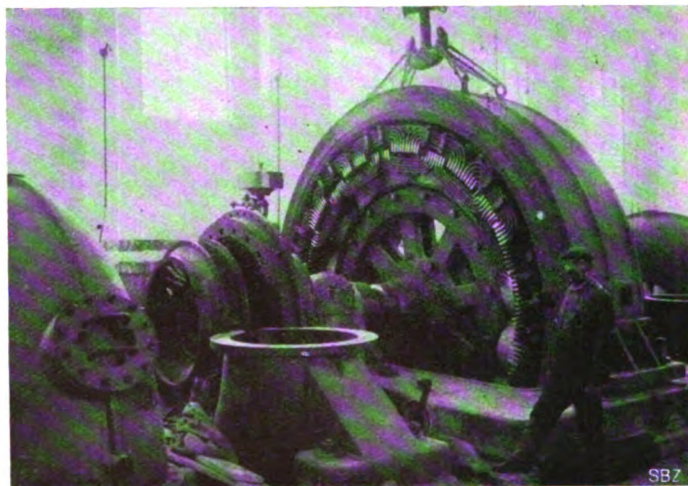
Maschinengruppe im Bau (5000 PS-Turbinen-Laufrad).
